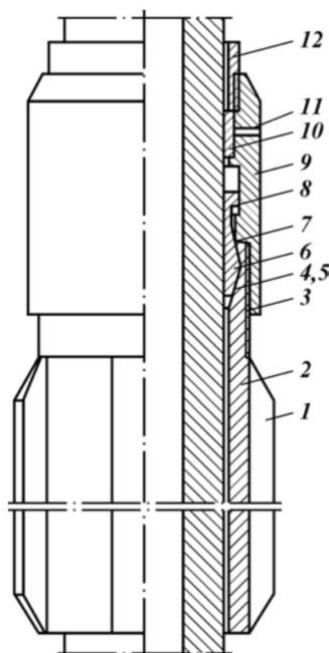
Центратор типа ЦБИ: 1 – ребра; 2 – корпус; 3 – резьба; 4 – расточка внутренняя; 5, 7 – конические поверхности; 6 – элемент зажимной; 8 – бурт; 9 – гайка запорная; 10 – элемент, расклинивающий; 11 – прорезь; 12 – втулка
